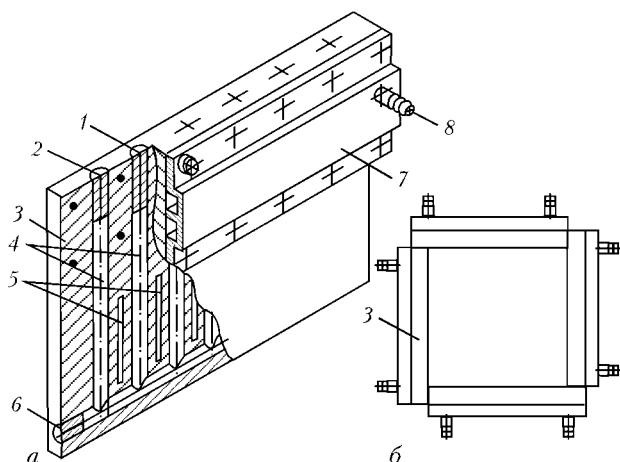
Конструкция секционной панели сборного кристаллизатора: а — в разрезе; б — схема сборки кристаллизатора; 1, 2 — заглушки; 3 — медная панель; 4 — каналы для протока охлаждающей воды; 5 — межсекционные прорезы; 7 — водяной коллектор; 8 — штуцер
